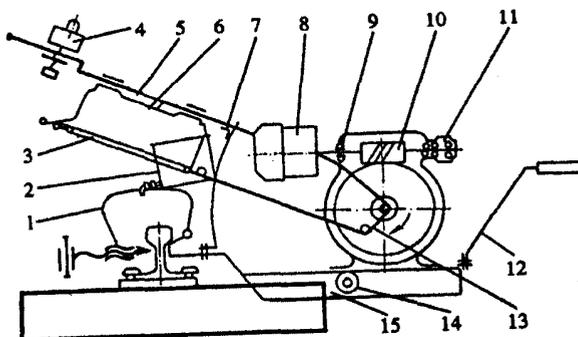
Схема рельсорезного станка РМ-3
